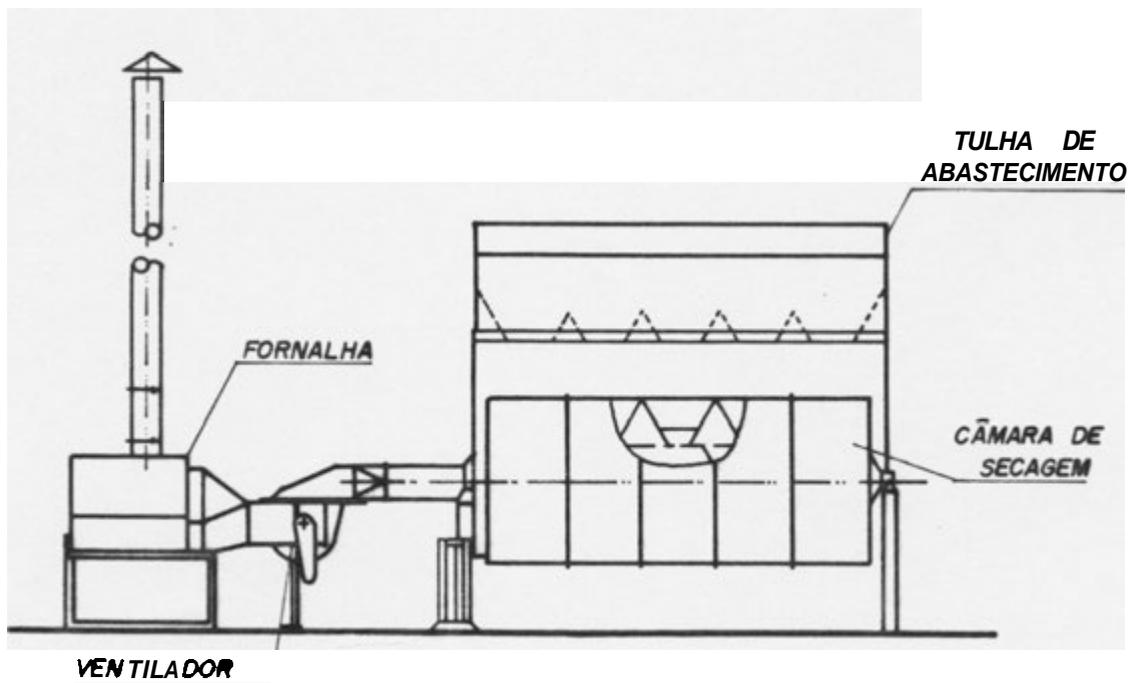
Secador Cilíndrico ou Tubular Rotativo
